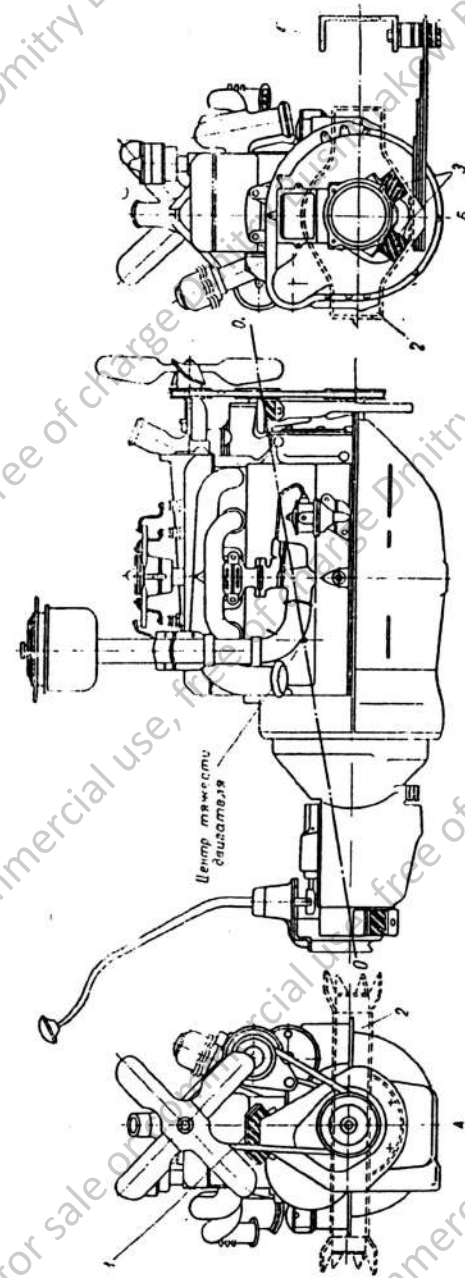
Крепление двигателя: 1 — передняя опора двигателя; 2 — подушка рамы; 3 — верхняя опора двигателя; 4 — полмерон
